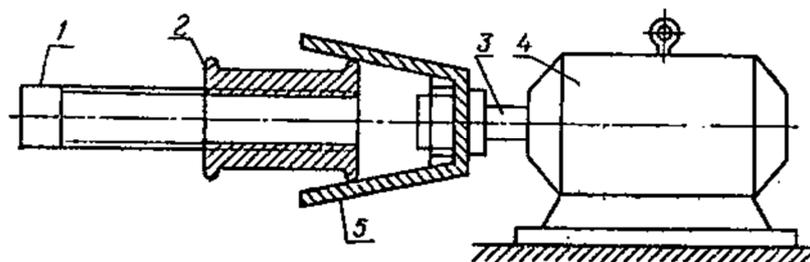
Стенд для испытания на герметичность арматуры и автопоилок
